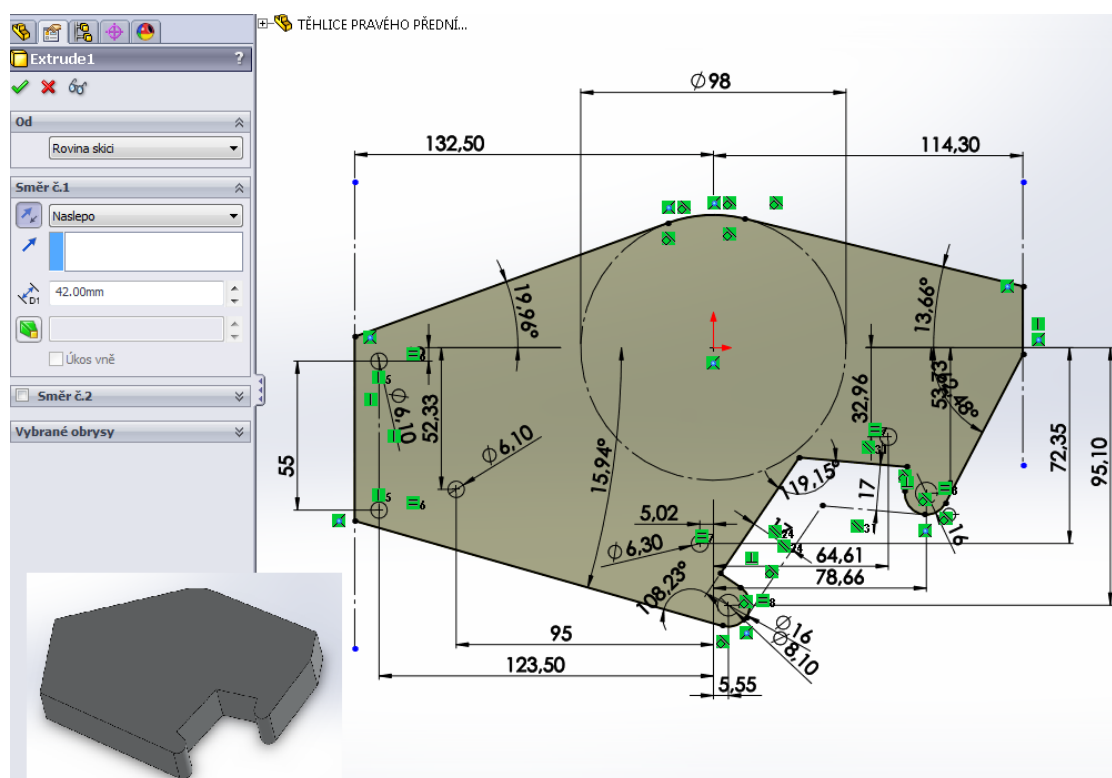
Uživatelské rozhraní parametrického CAD softwaru SolidWorks 2012.
